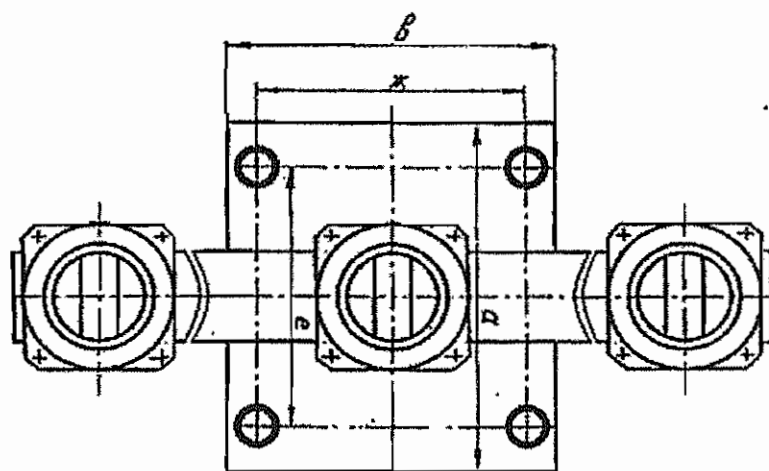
Траверсы типа ТПО-12,5 для промежуточных опор воздушных линий электропередачи на напряжение 10, 20, 35 кВ и типа ТАУО-12,5 для анкерно-угловых опор линий на 10 кВ. Вид сверху
